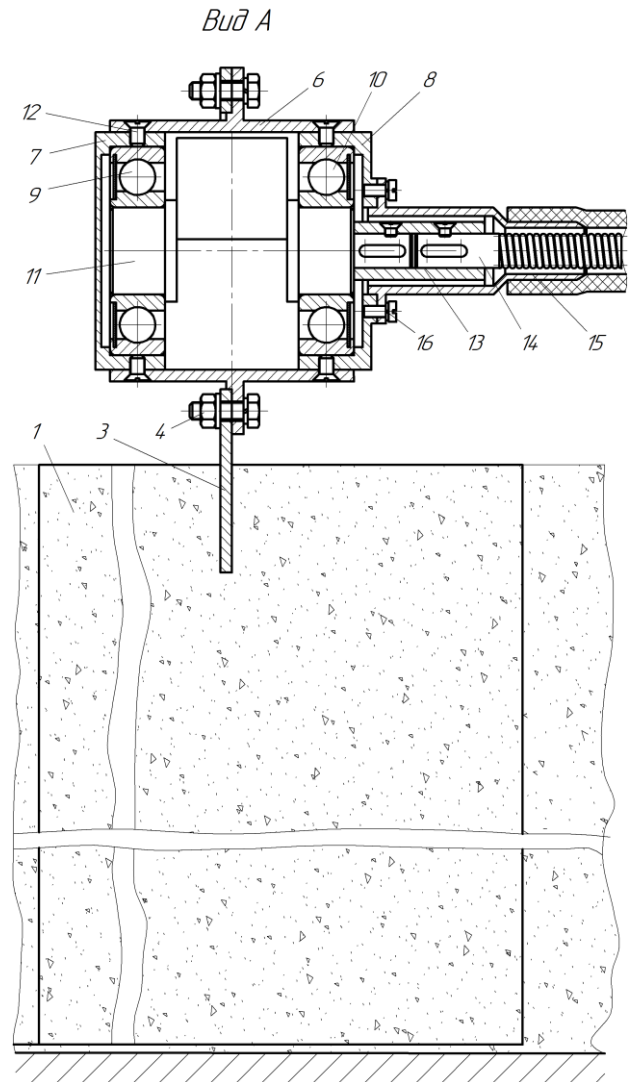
Общий вид плоскостного глубинного уплотнителя (вид А на рис. 1)
